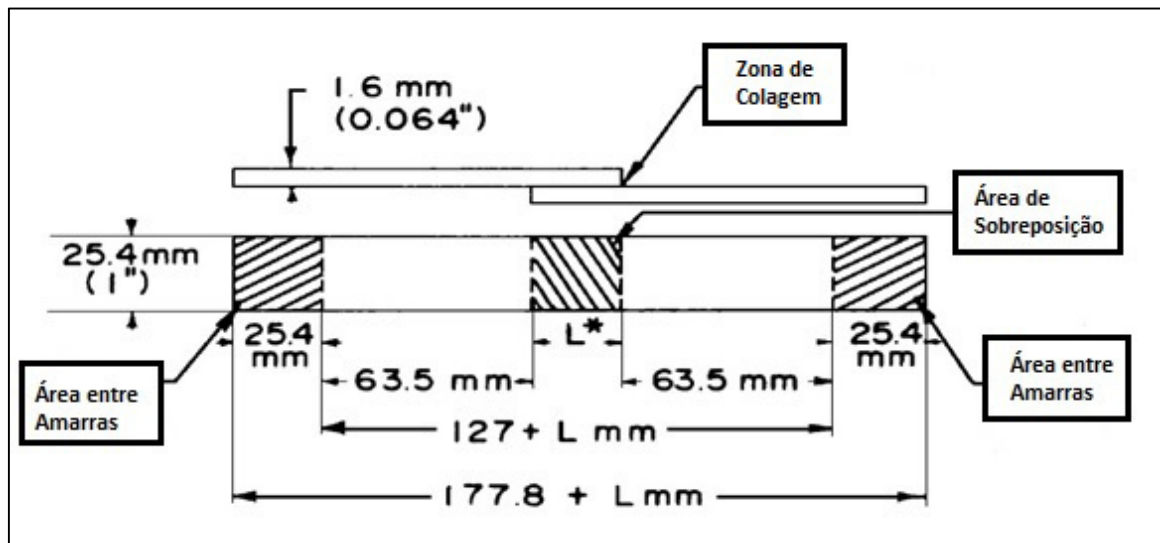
Dimensões e forma da junta. Adaptado de [62]
